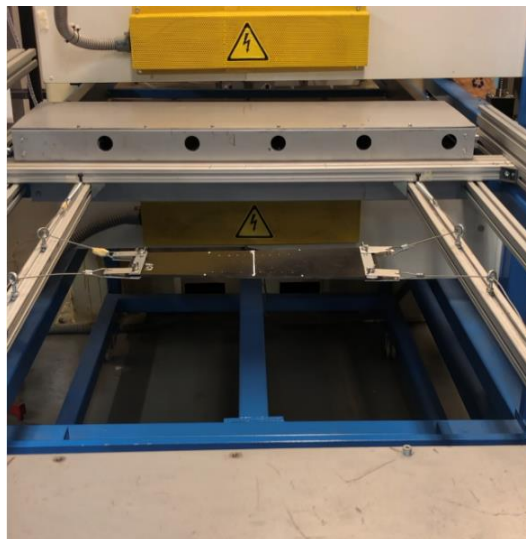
Blank* posicionado no carro através do *blank-holder
